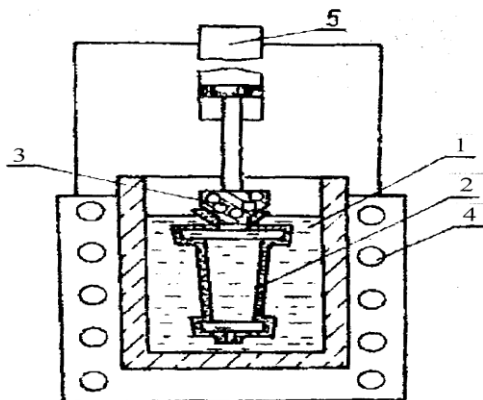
Схема установки для получения отливок вытягиванием из расплава
